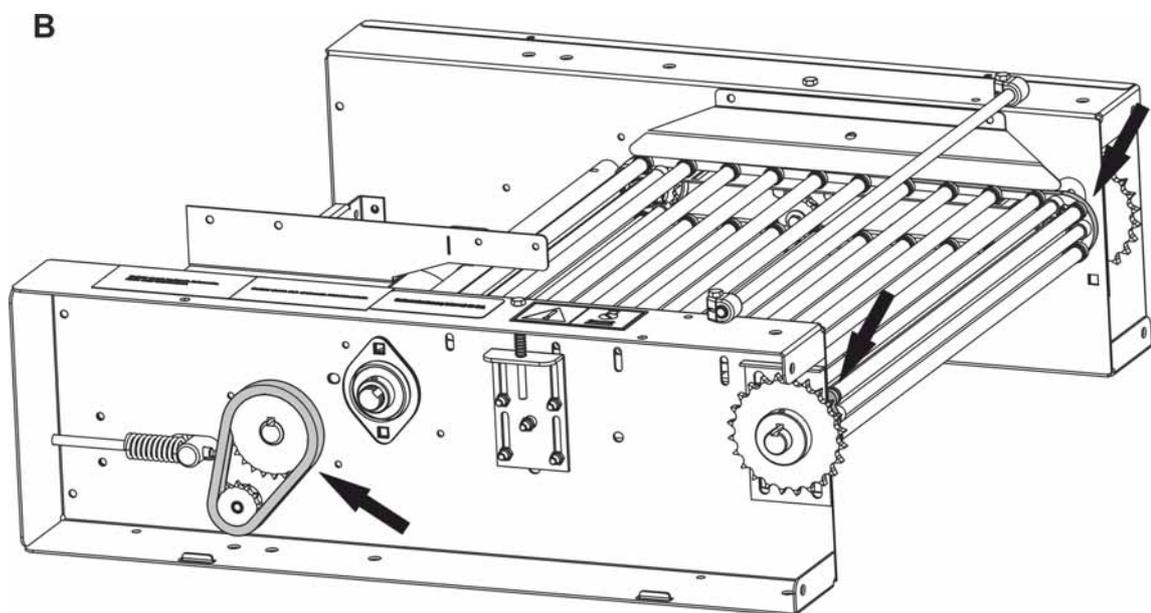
Detail B Schmierpunkte Stabförderer Rollenketten
